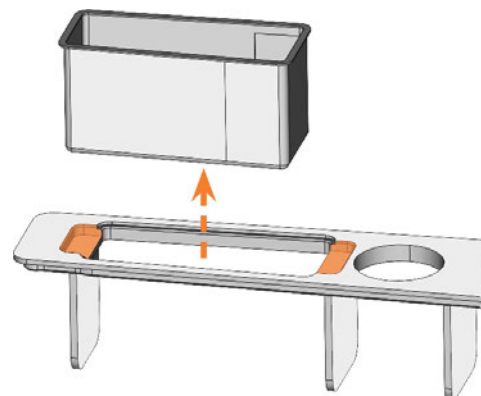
RETIRER LE PANIER-FILTRE (SURFACES RENFORCÉES DE COULEUR ORANGE)
